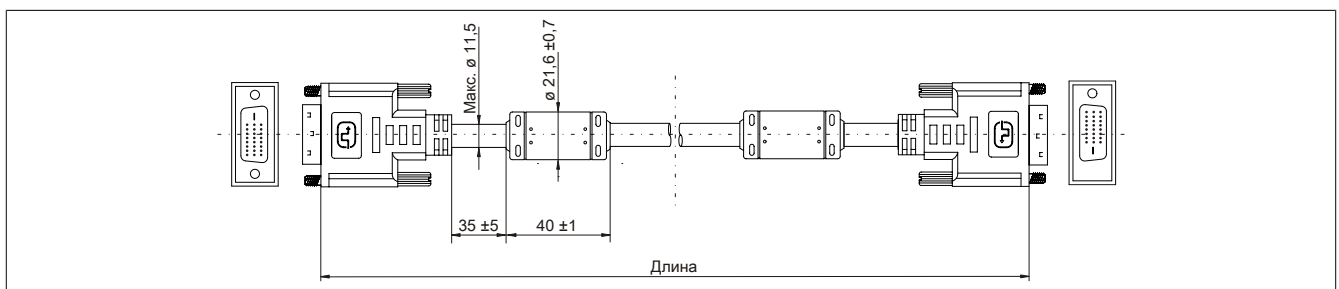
5CASDL.0xxx-00 — Размеры
